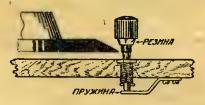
Простое верньерное приспособление к обычным конденсаторным ручкам.
